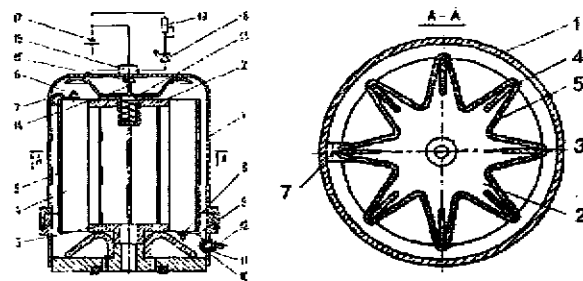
Регенерируемый фильтр для очистки масла двигателя внутреннего сгорания: 1 – корпус фильтра; 2 и 3 – торцевые диски; 4 – пластины; 5 – фильтрующая углеродная ткань; 6, 8 и 12 – клеммы; 7 – упругий контакт; 9 – соединительный проводник; 10 – текстолитовая втулка; 11 – текстолитовая шайба; 13 – перепускной клапан; 14 – стержень; 15 – постоянный магнит; 16 – магнитоиндуктивная интегральная микросхема; 17 – источник питания; 18 – светодиод; 19 – регулируемый резистор
